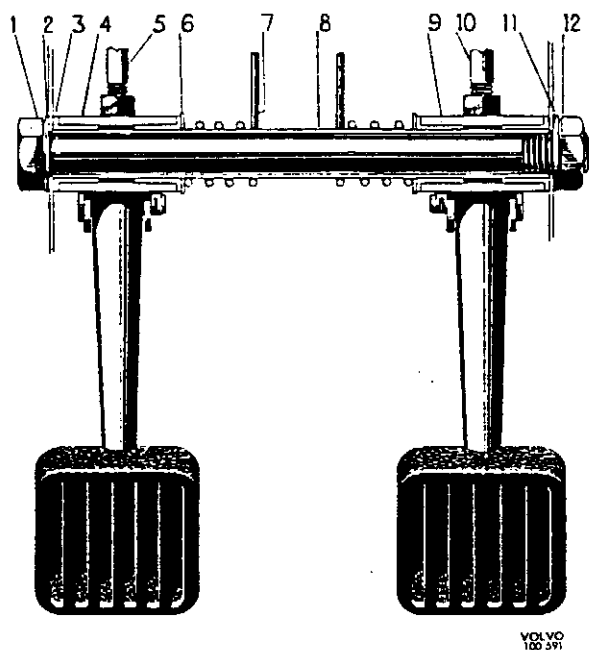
Pedalaufhängung, 120, 1800, Ausf. II
